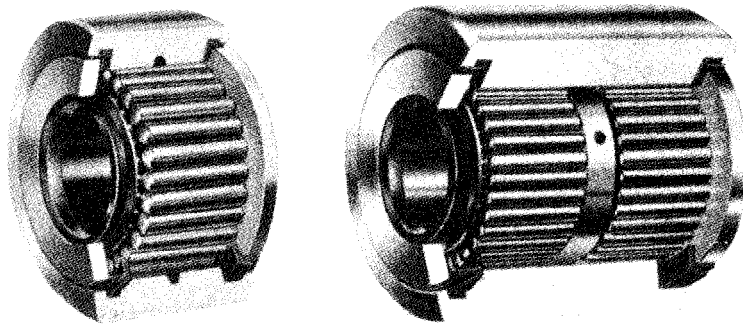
Cojinete de rodamientos cilíndricos. (Hoover-NSK Bearing Company, Ann Arbor, Mich.)
